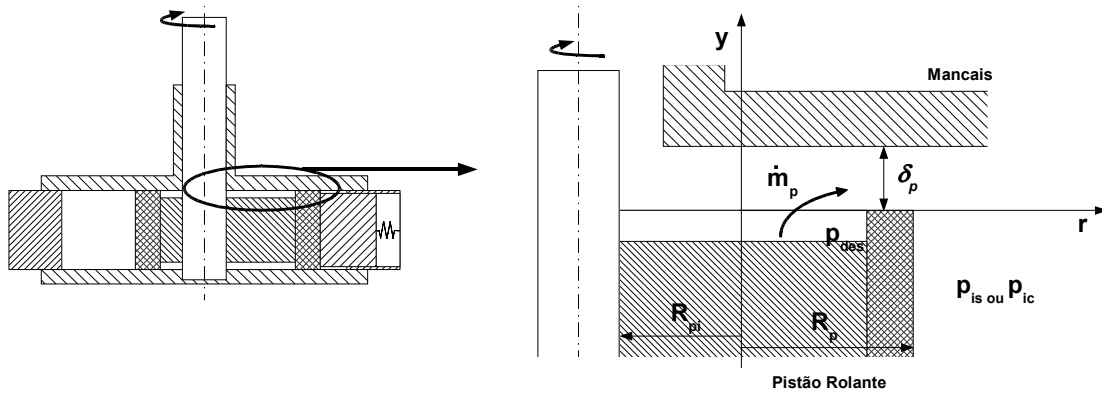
Região da folga de superfície entre pistão rolante e cilindro - compressor de pistão rolante.
